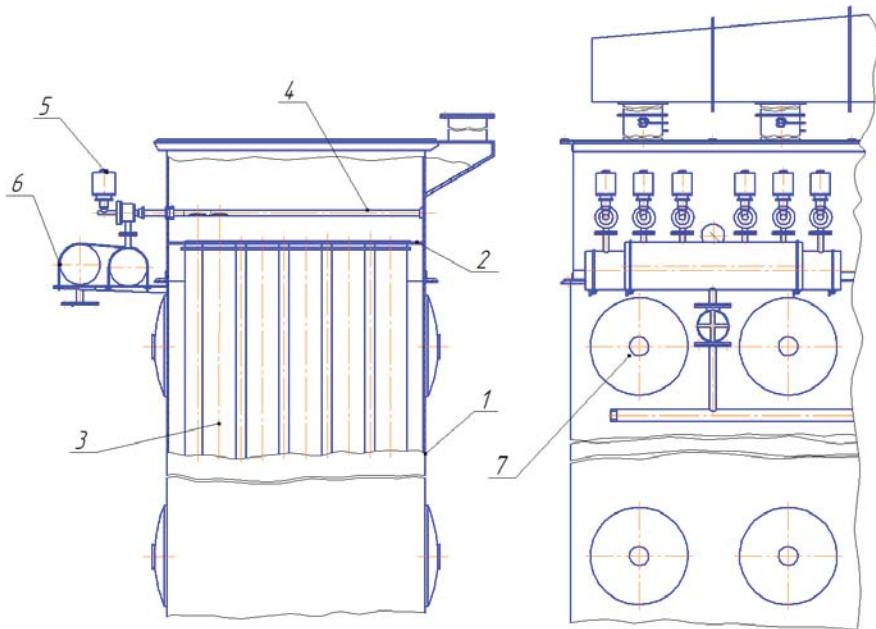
Секция модернизированного фильтра ФВ-60: 1 – корпус; 2 – решетка; 3 - фильтровальные рукава; 4 - продувочные трубы с соплами; 5 - электромагнитные клапаны; 6 – ресивер; 7 - люки
